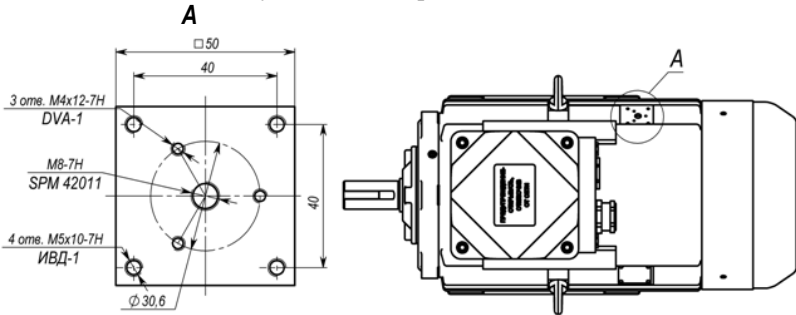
Место под установку вибродатчиков ИВД-1, DVA-1 и SPM 42011 на корпусе двигателя
